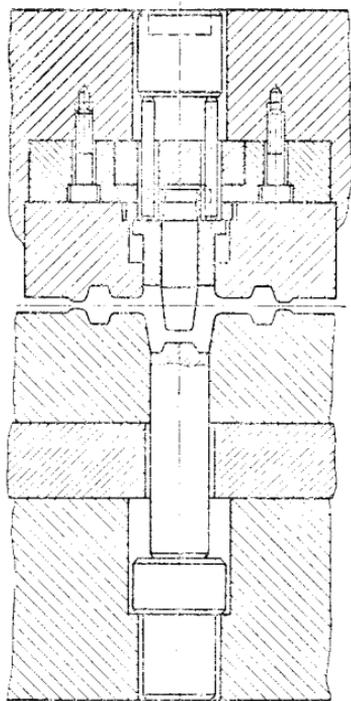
Круглый (нижний) и кольцевой (верхний) выталкиватели из окончателного ручья для шестерни, показанной на рис. 206
